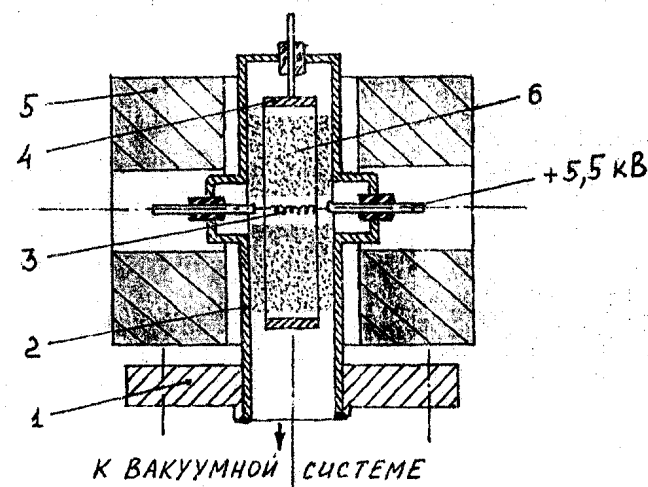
Схема конструкции манометрического преобразователя ПММ-46: 1 - присоединительный фланец; 2 - корпус преобразователя из немагнитной стали; 3 - нитевидный анод; 4 - полый цилиндрический катод; 5 - съемный постоянный магнит; 6 - разрядный промежуток
